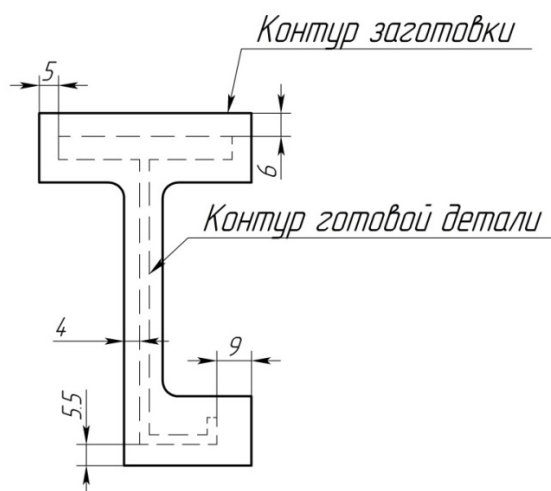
Поперечное сечение заготовки и готовой детали (сегмента шпангоута)
